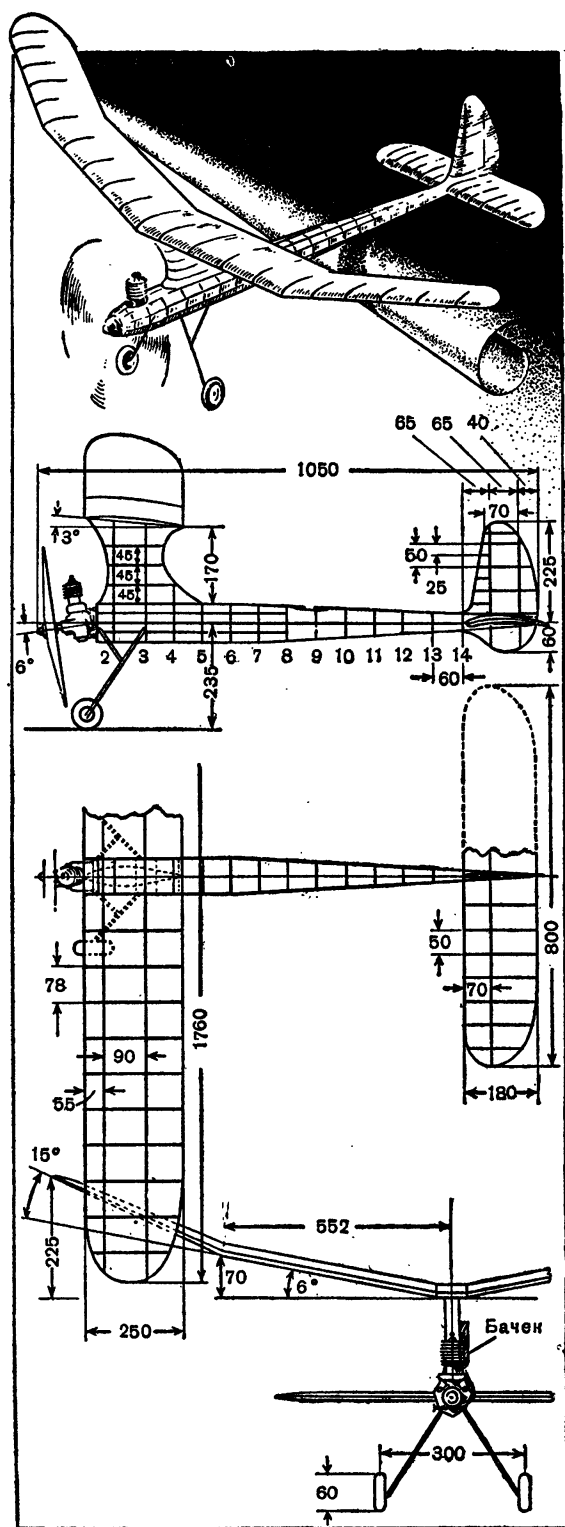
Эскизный чертеж парящей модели самолета с механическим двигателем.
